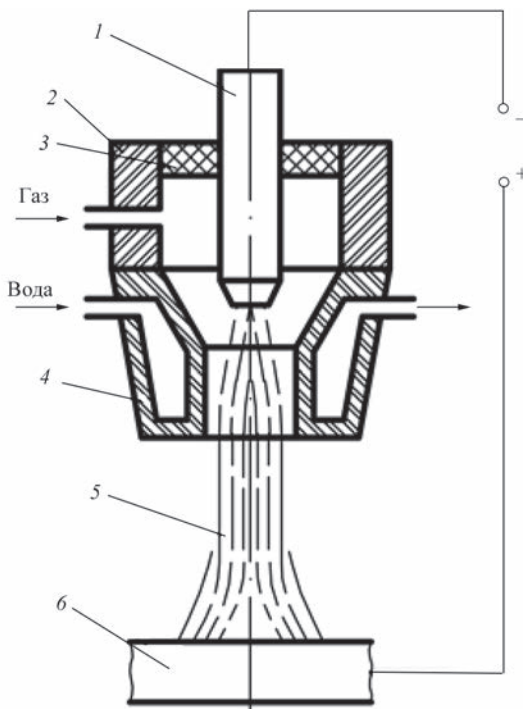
Принципова схема дугового плазмотрона прямої дії: 1 — стержневий електрод; 2 — корпус; 3 — ізолятор; 4 — сопло; 5 — плазмова дуга; 6 — тіло, що нагрівається
